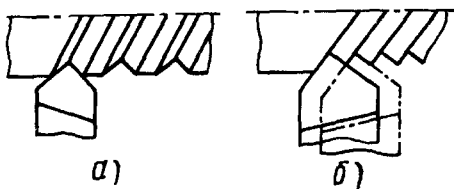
Поверхности детали, сформированные резцом:
